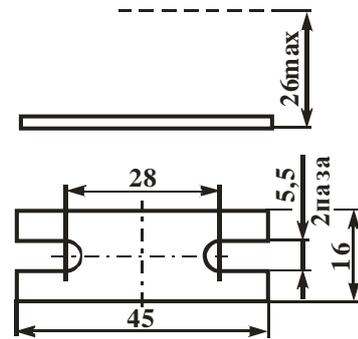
б – Габаритные и присоединительные размеры ЭЗ1-Бх
